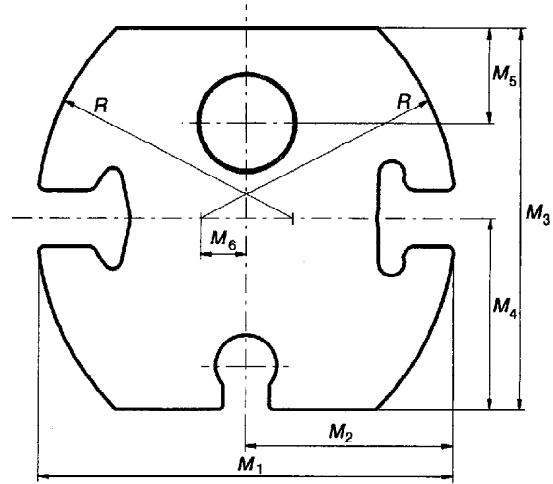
Dimensions du calibre pour la tige à rotule de type 22N
